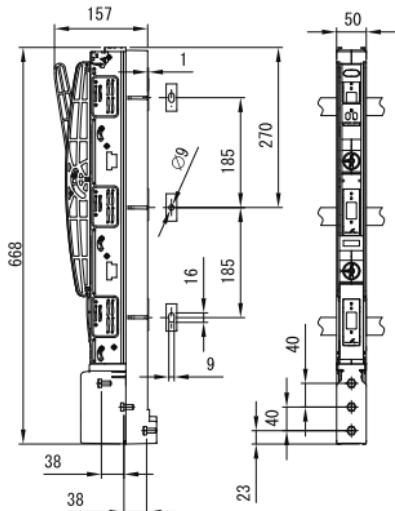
Габаритные размеры ПВР-1 160 А / Figure A.1 – Overall dimensions of PVR-1 160 A
